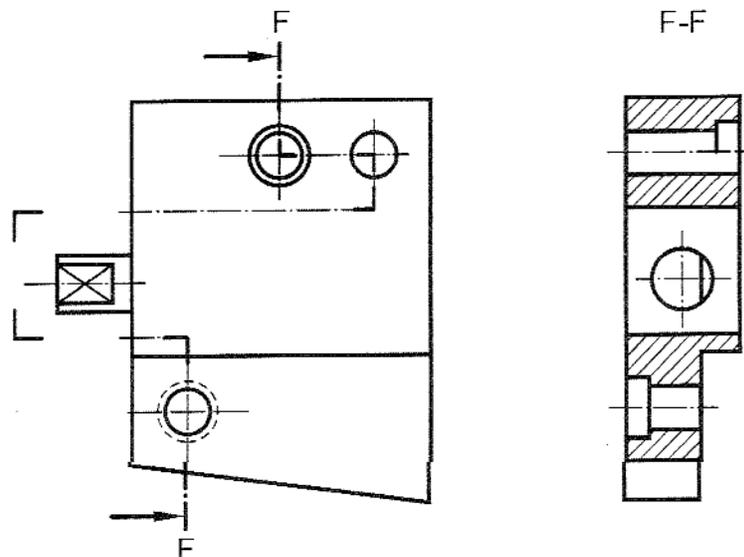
Plano de corte posicionado parcialmente fuera del objeto
